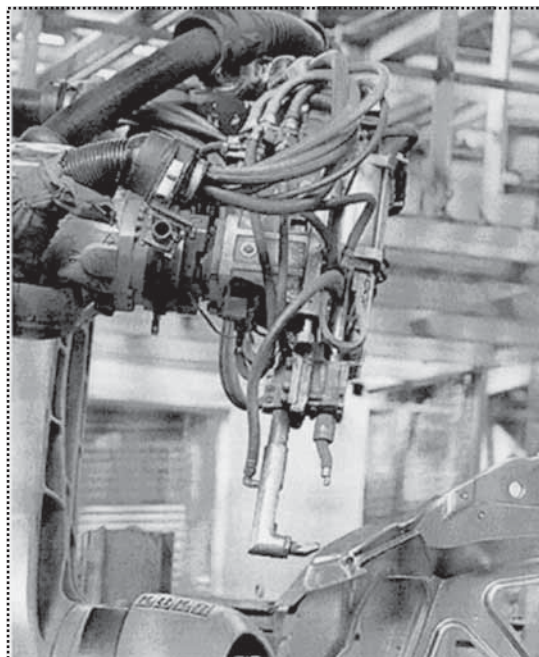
Подвесной сварочный робот со штоковыми клещами для контактной точечной сварки кабин автомобилей семейства "Газель"
